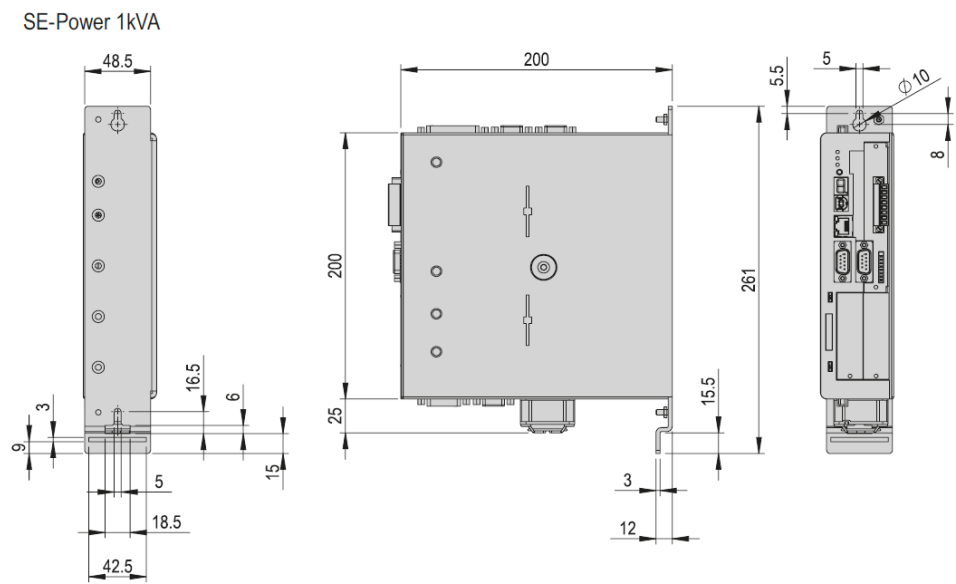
Installation - SE-Power für Schaltschrank Montage
